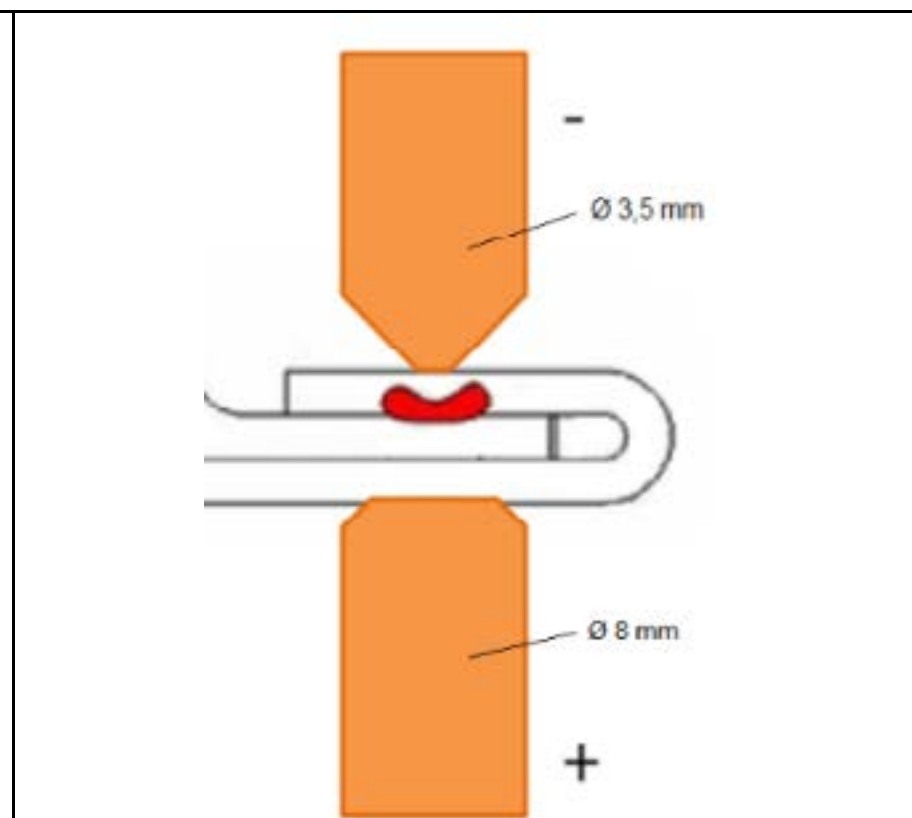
Posicionamento dos eletrodos durante a soldagem
